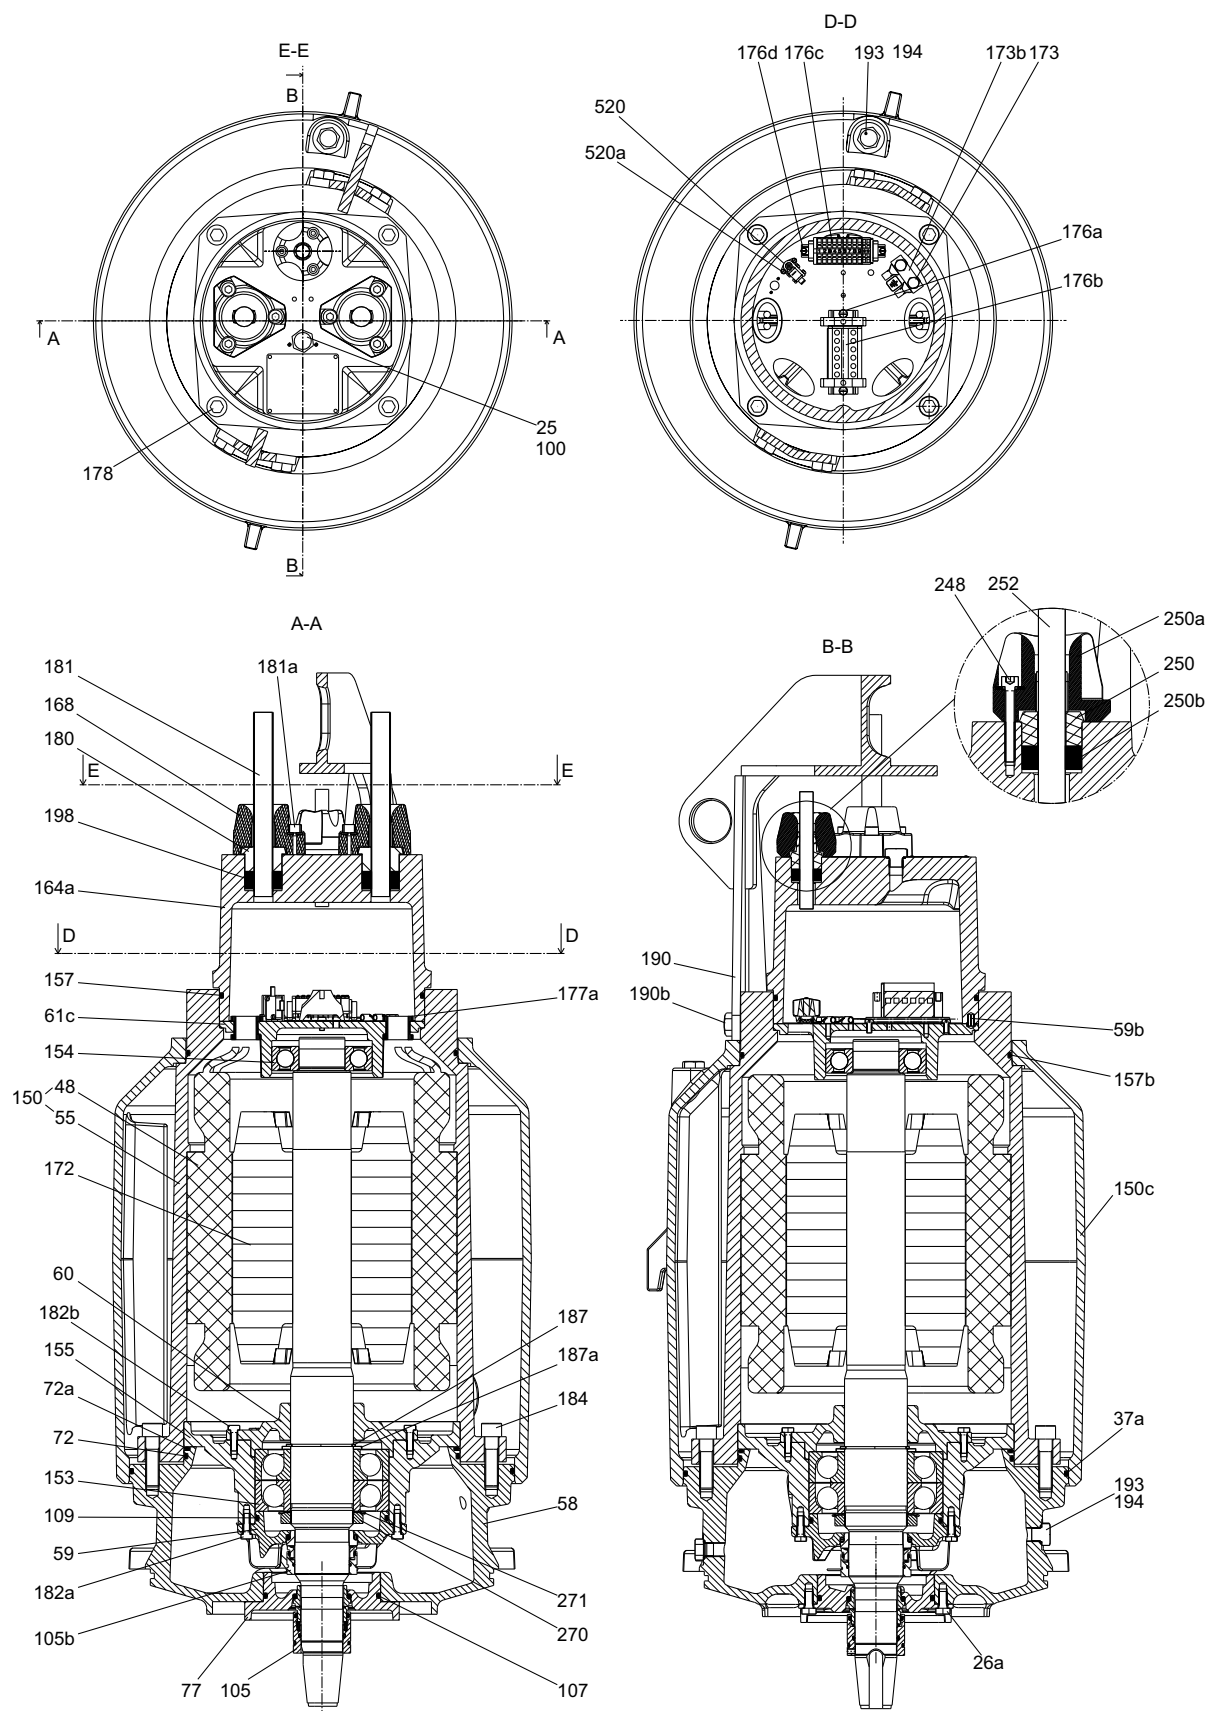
Стандартный электродвигатель с охлаждающим кожухом
